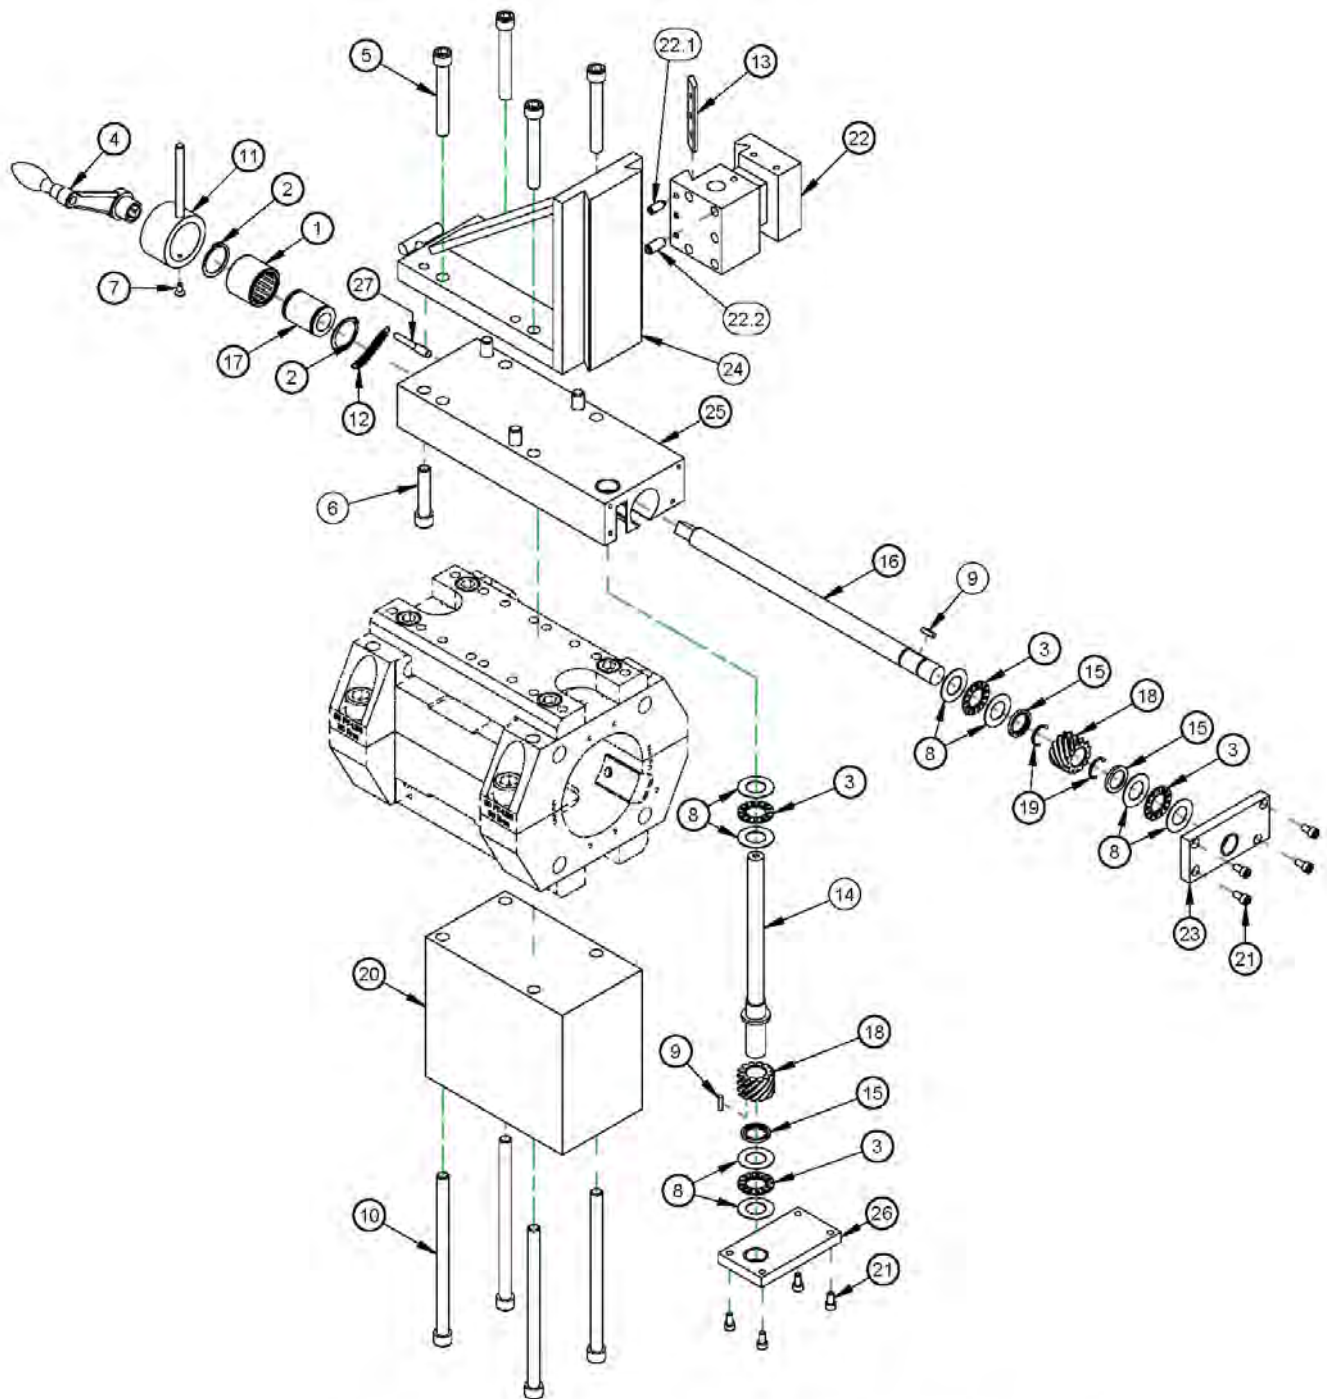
Накладные блоки в сборе, перечень деталей (кат. № 81252)
